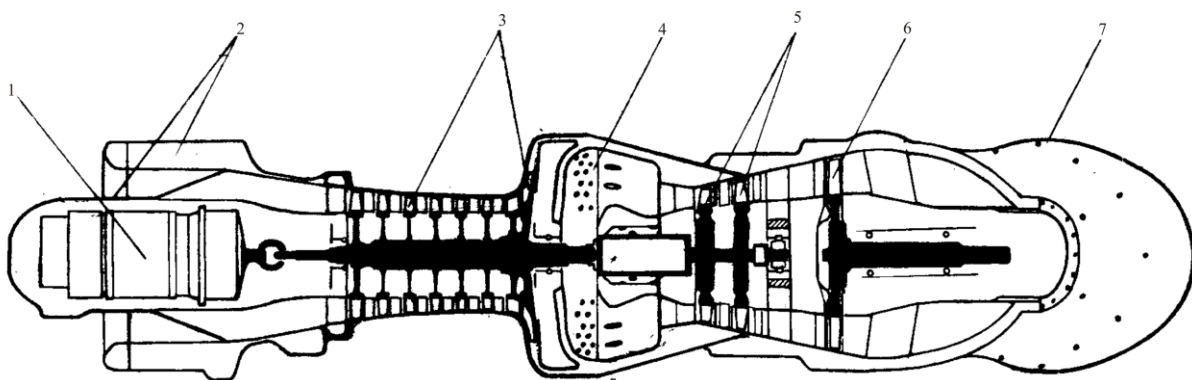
Схема турбовинтового двигателя ГТД-3Ф:
